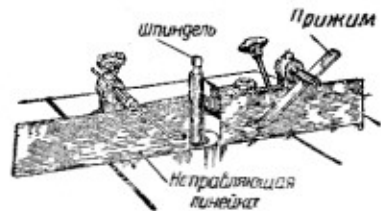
Стол фрезерного станка с направляющей линейкой и прижимом
